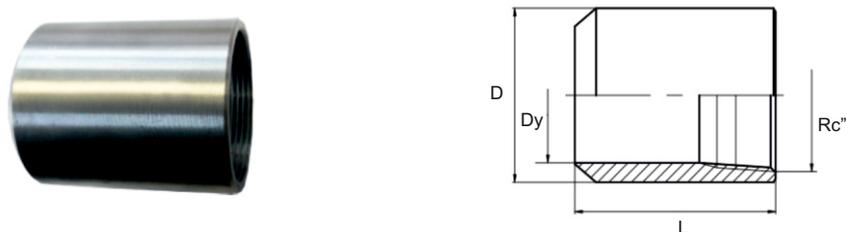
Муфта для соединения РВД с трубопроводом
